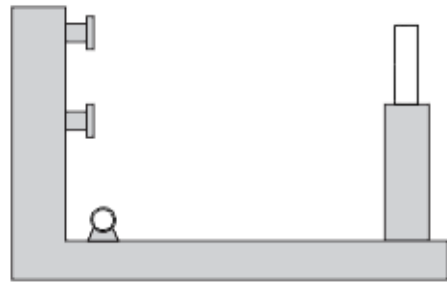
Matriz de soldadura de un marco de bicicleta
